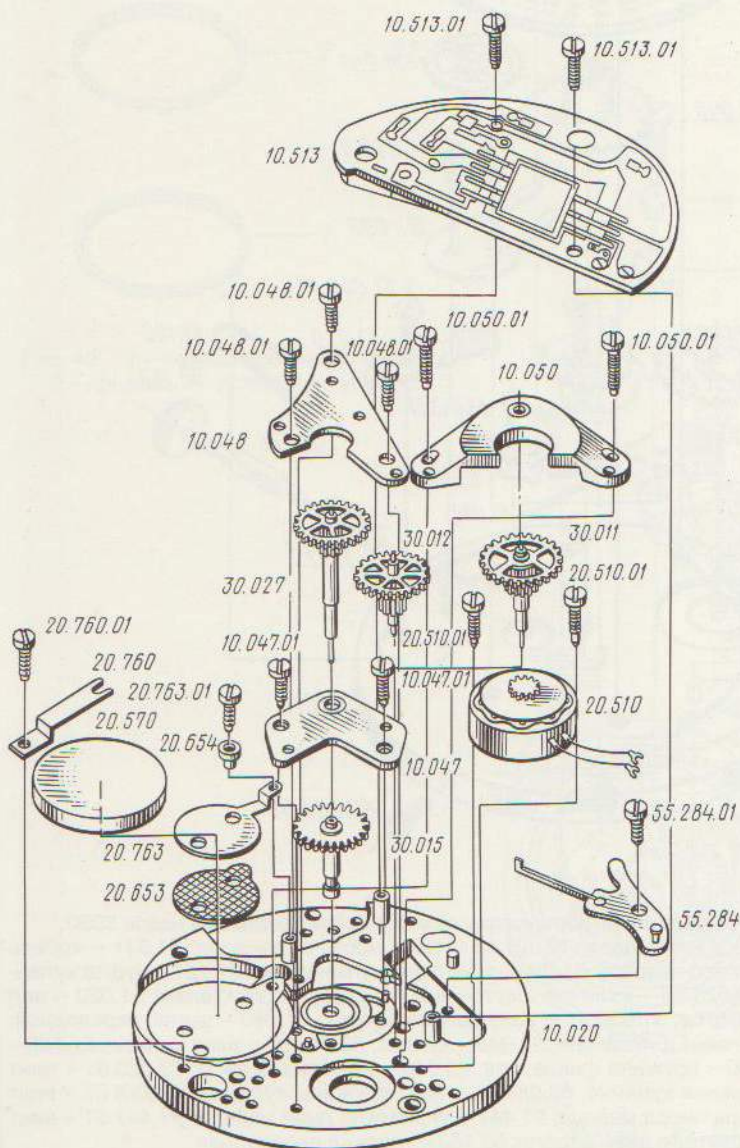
Детали и сборочные единицы механизма часов 3050:
